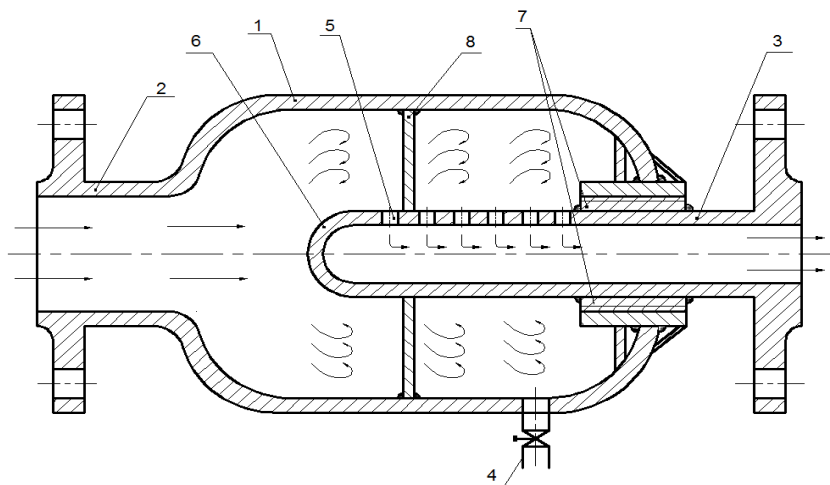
Устройство для очистки газа от жидких и твердых примесей:
